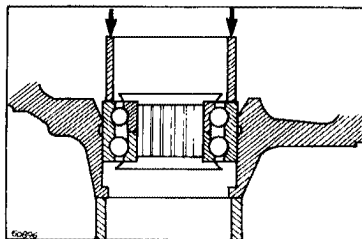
Установка подшипника ступицы с помощью трубчатой оправки
